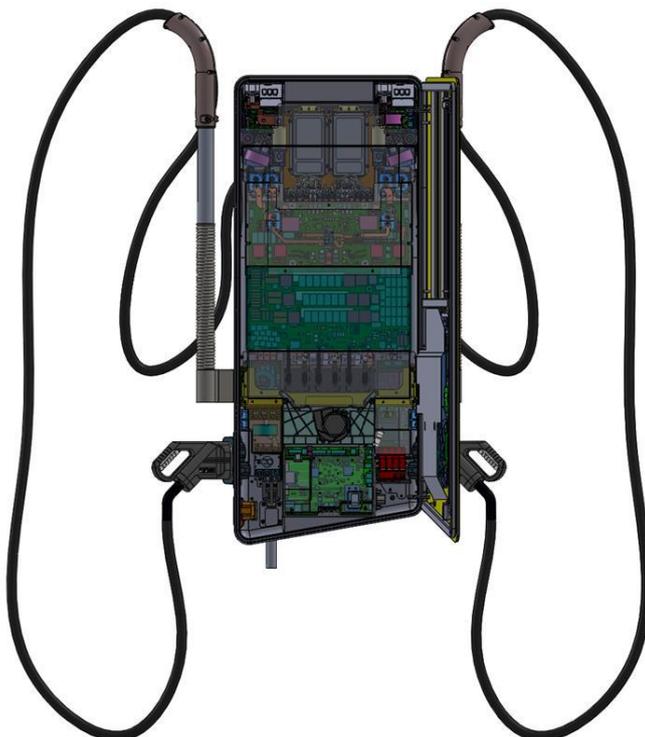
HYC_50 Ansicht mit geöffneter Fronttür (Beispiel mit 2x DC-Ladekabeln)
